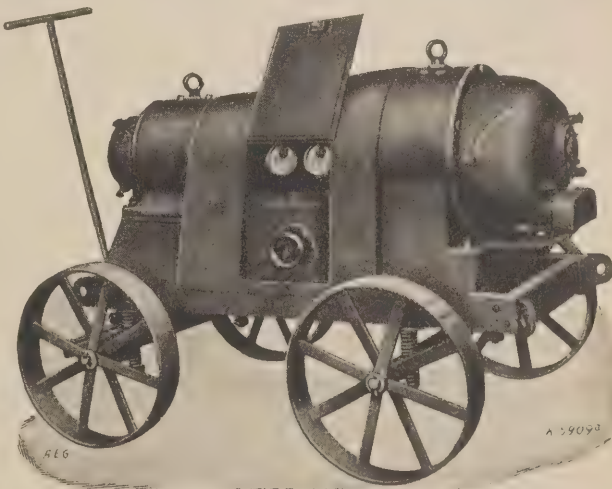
Fahrbarer Lichtbogen-Schweißumformer Type HN 133 VGN 75 bzw. VDNM 75/4.
